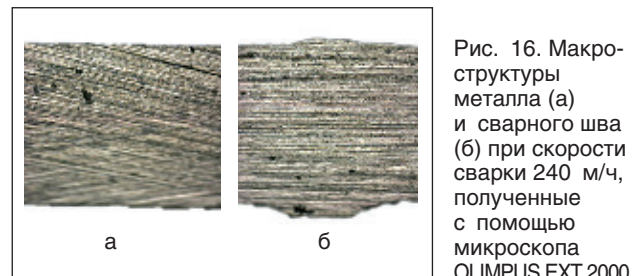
Макроструктуры металла (а) и сварного шва (б) при скорости сварки 240 м/ч, полученные с помощью микроскопа OLIMPUS EXT 2000
